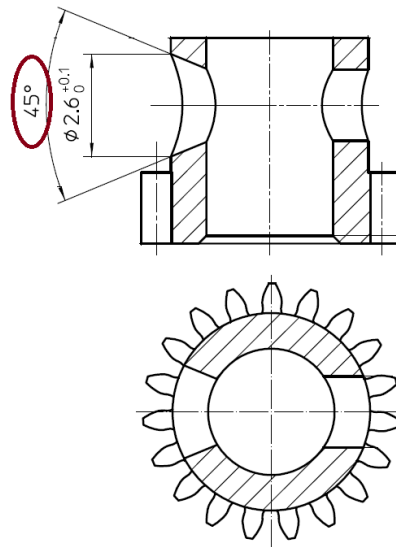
Secção do desenho técnico do carreto, ângulo de 45°
